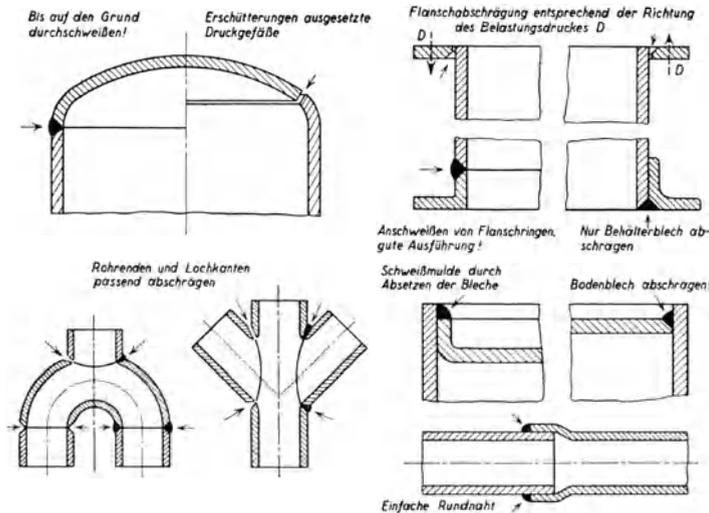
Rohrverbindungen durch Schweißen.
